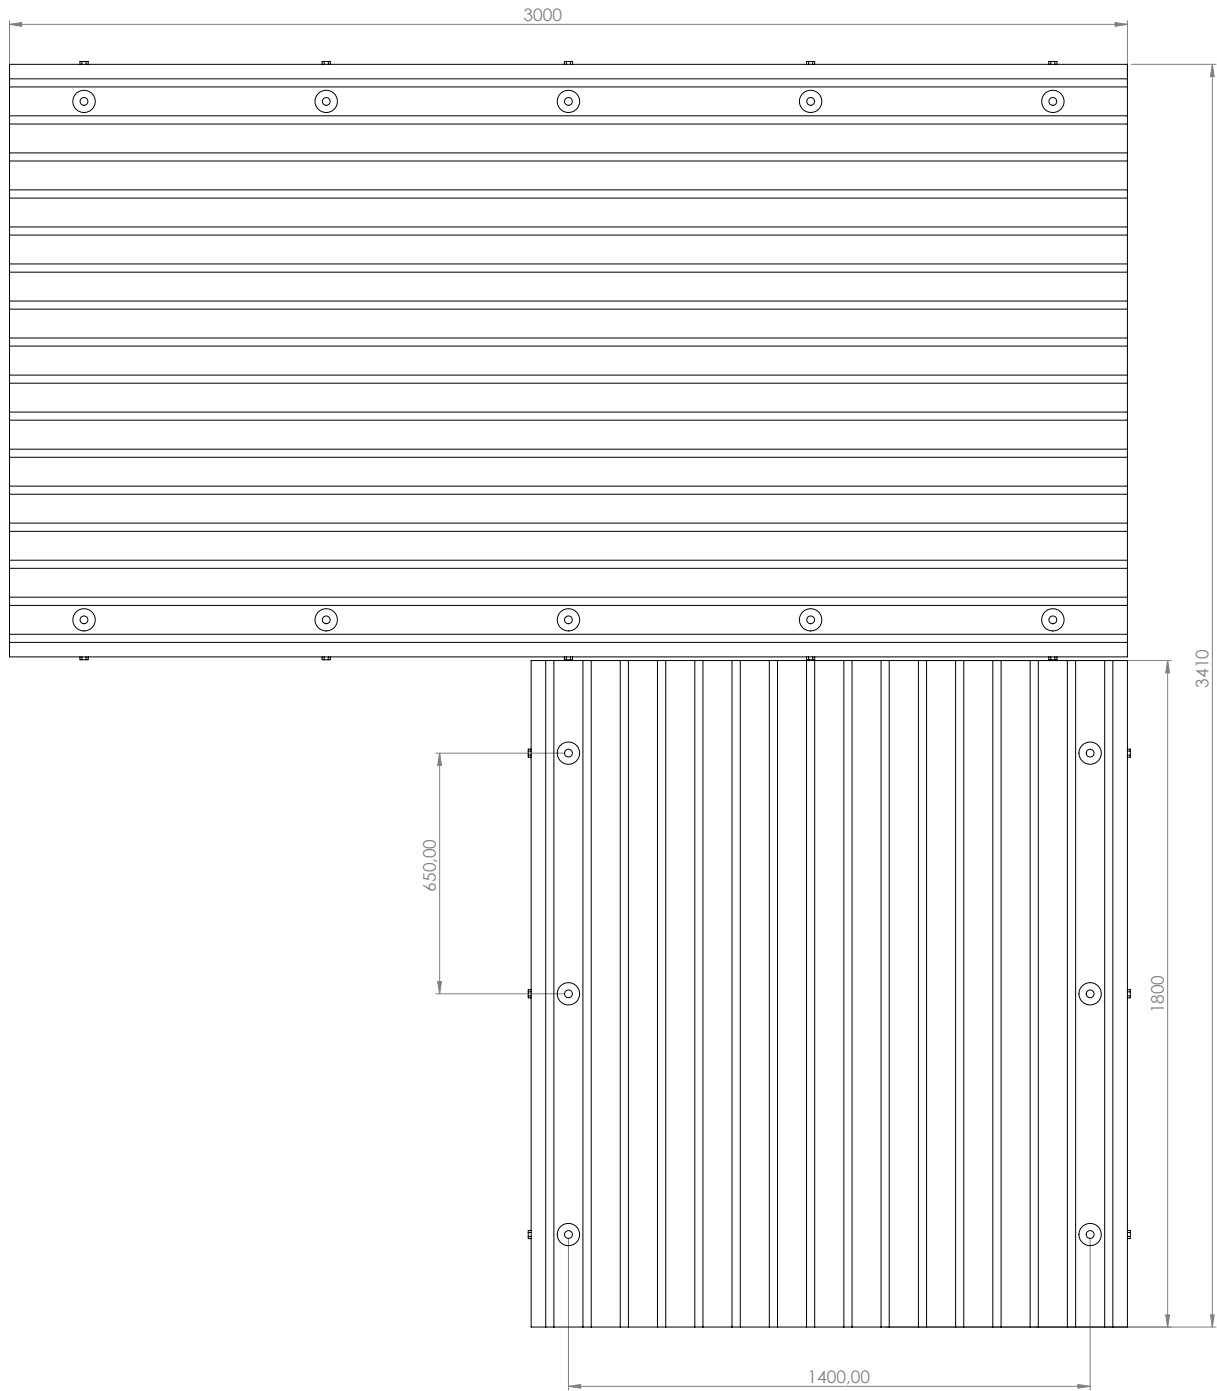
Zeichnungsableitung 2- Prüfstand (Maschinentisch)
